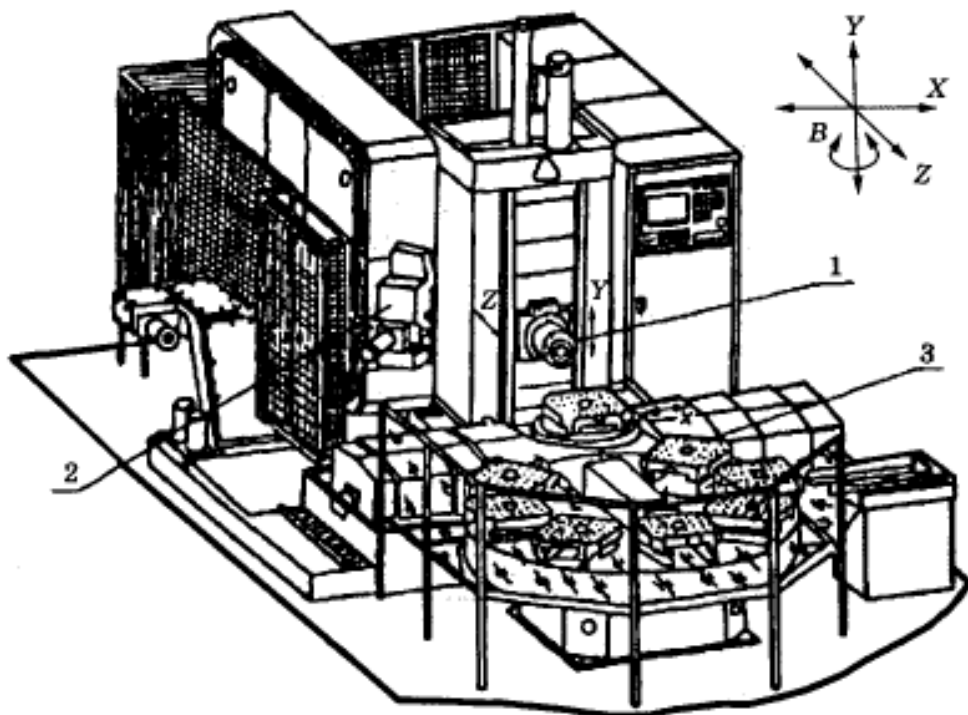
Гнучкий виробничий модуль для обробки корпусних деталей
